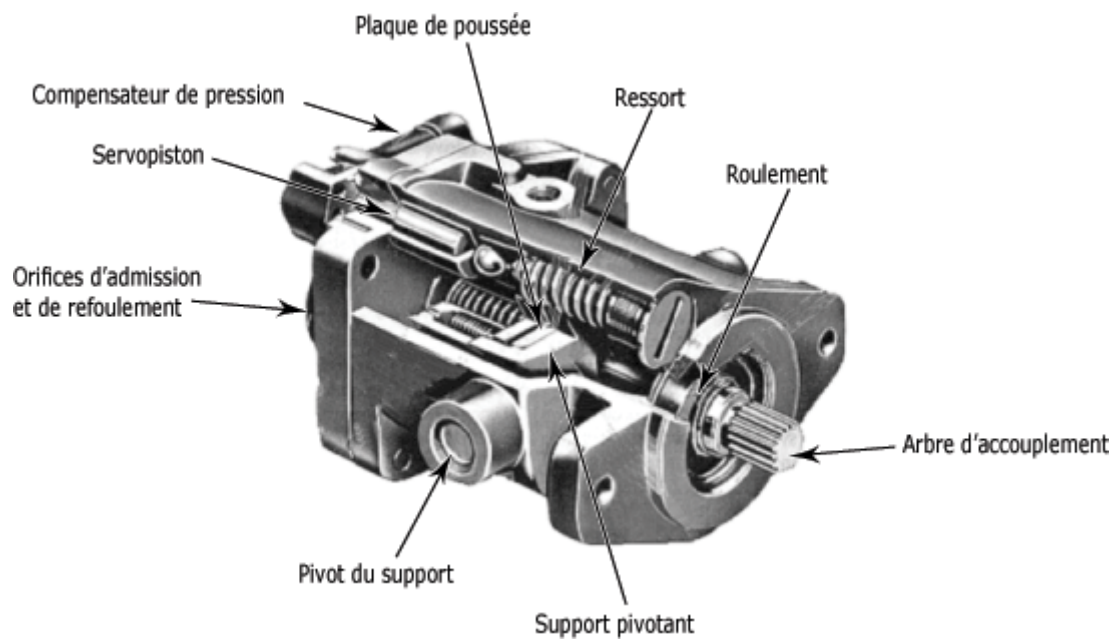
Vue en coupe d'un moteur hydraulique.
